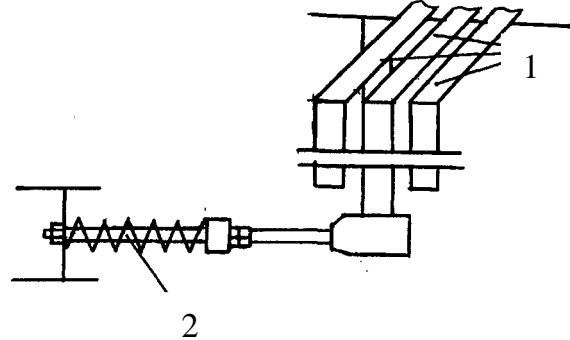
Механизм регулировки перекрытия планок:
